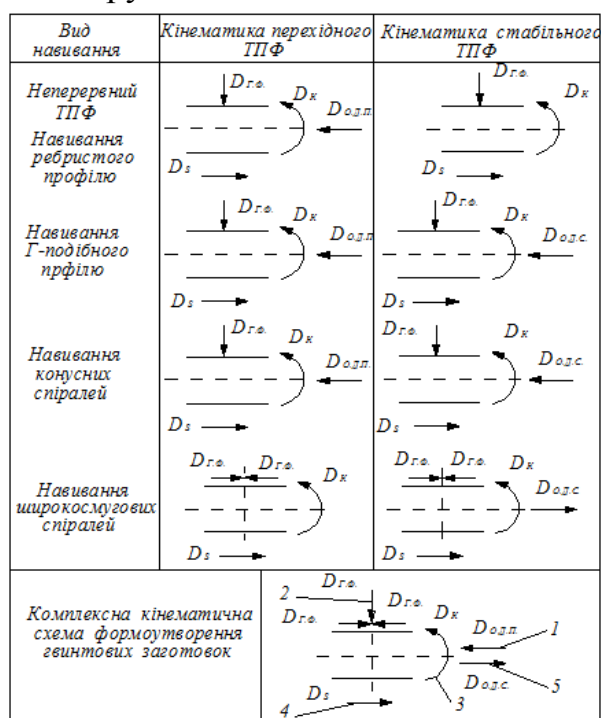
Кінематика формоутворення гвинтових заготовок
